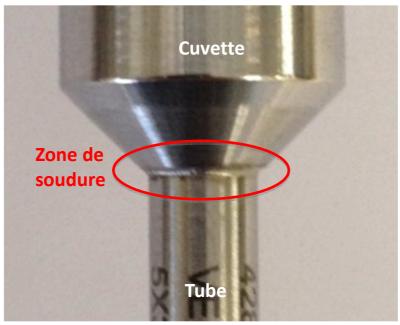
Inspection de la soudure : Correcte, aucune trace de dommage
